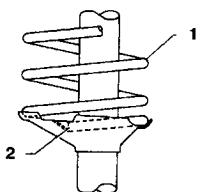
Положение установки пружины - стойка задней подвески (См. Раздел 11)
